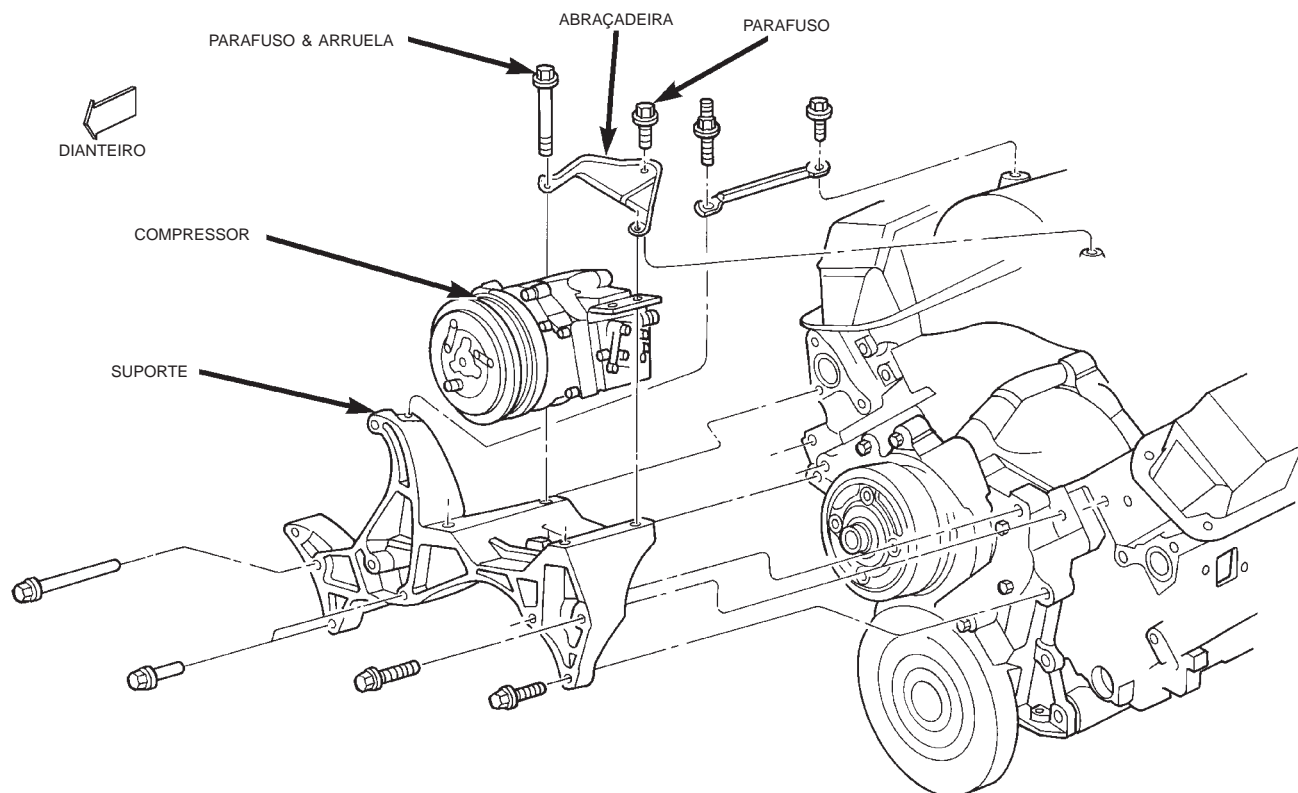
Remoção/Instalação do Compressor - Motor 2.5L
